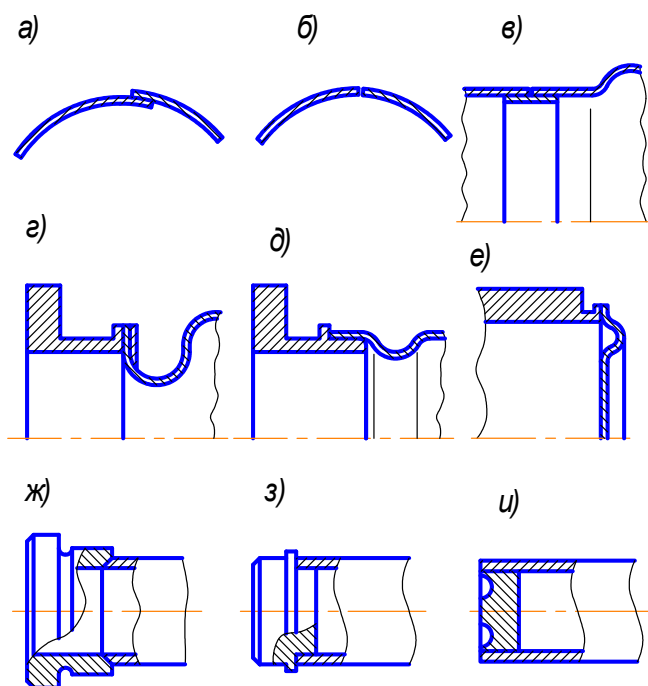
Типы сварных соединений тонкостенных изделий
